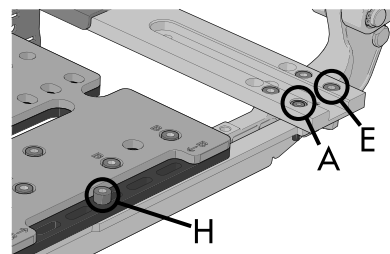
Die vordere Befestigung (H), M4x20-Schraube (A) mit der Buchse und M6x20 (E) mit der Unterlegscheibe und Sicherungsmutter an der hinteren Befestigung.
